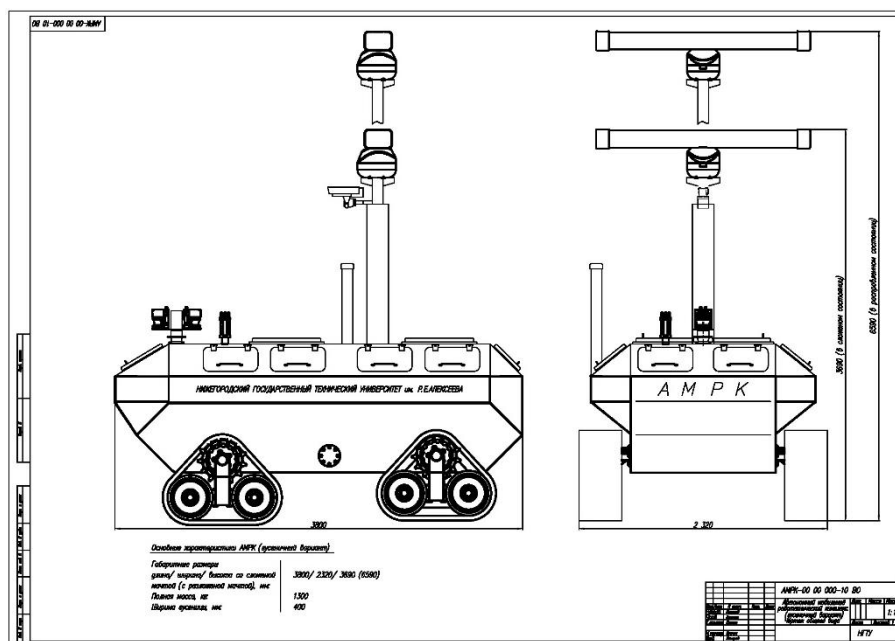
Общий вид шасси МРК с гусенично-модульным движителем
